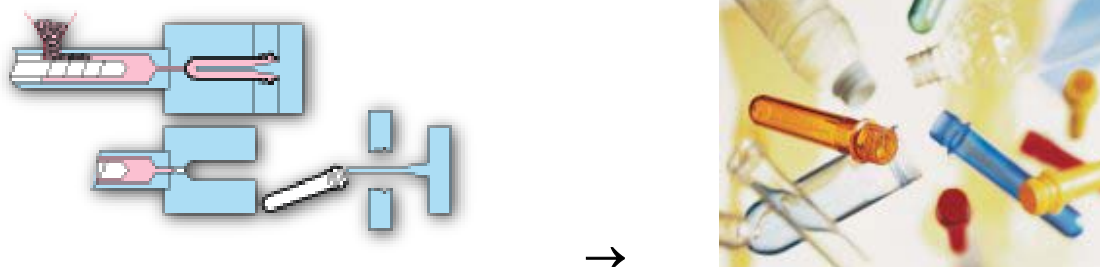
Produção das pré-formas pelo processo moldação por injeção.
